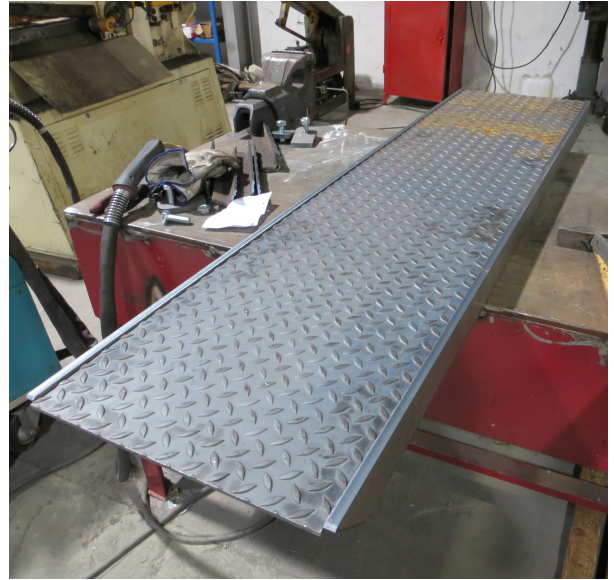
Plataforma com as barras superiores soldadas
